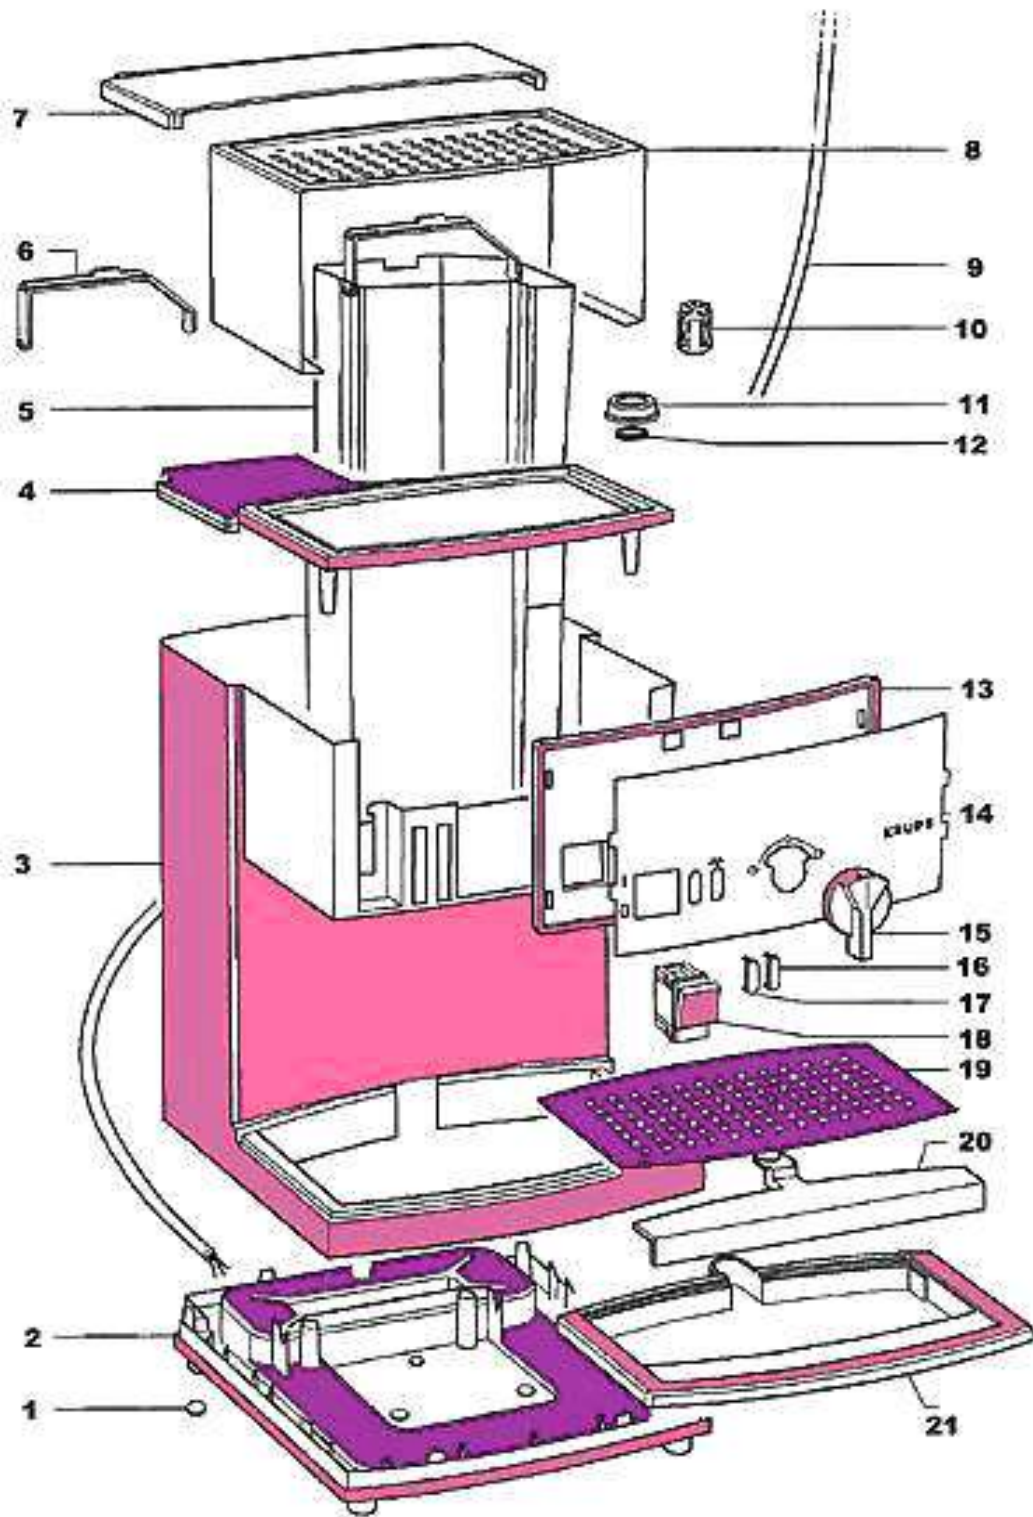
Елементи конструкції кавоварки (корпус)
